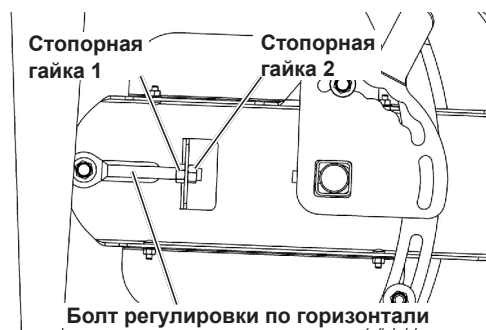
Регулировка смещения барабана питающего шнека вперед или назад
